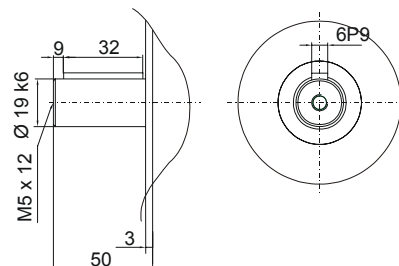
Mechanische Abmessungen der Motorenreihe JK6
